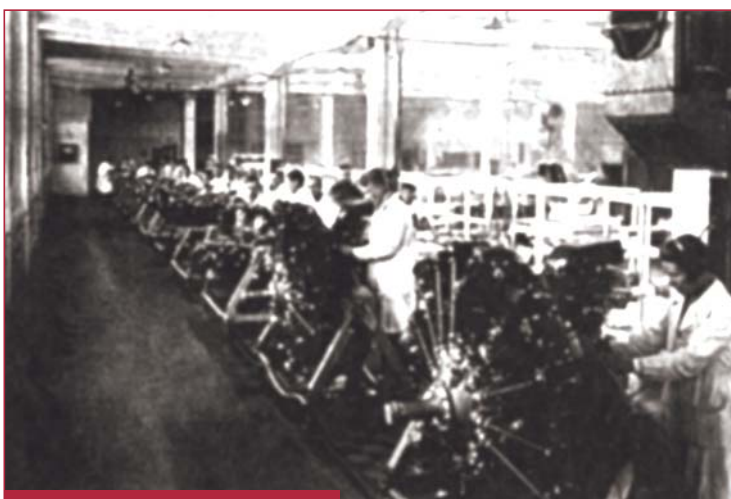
Сборка моторов M-25B : детали кладутся друг на друга, хотя бы
